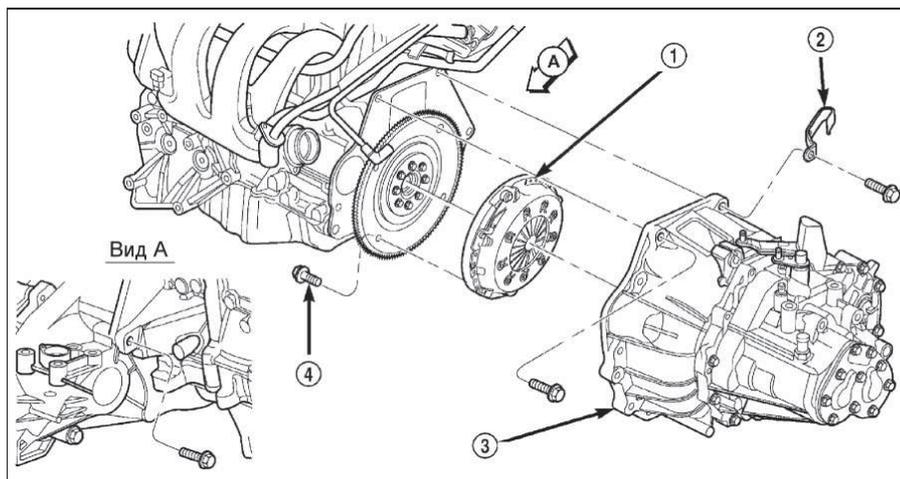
а. Механическая коробка передач. Снятие и установка - типичный пример. 1 - сцепление, 2 - клипса, 3 - коробка перемены передач, 4 - болт крепления сцепления (4 шт.).
